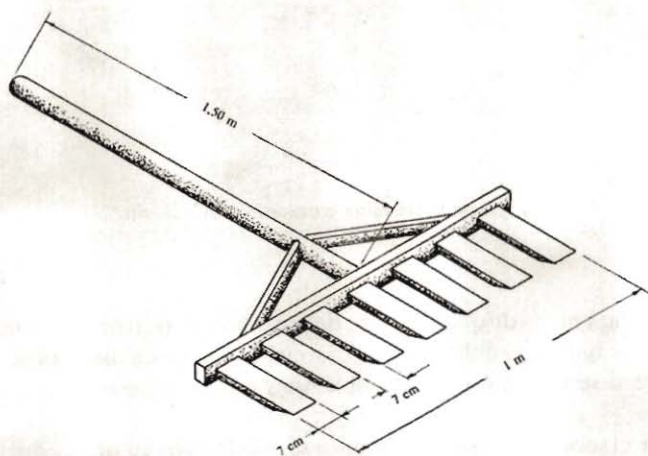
Rastrillo de madera para coltear los trozos de yuca sobre el piso de concreto.
